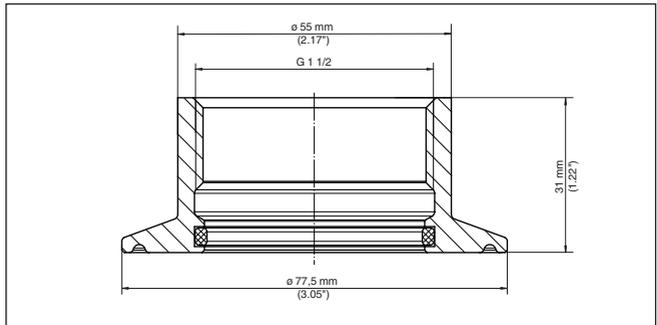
Dimensiones adaptador de rosca G1½ (DIN 3852-X) a Clamp 2½" (DIN 32676, ISO 2852) PN 16
